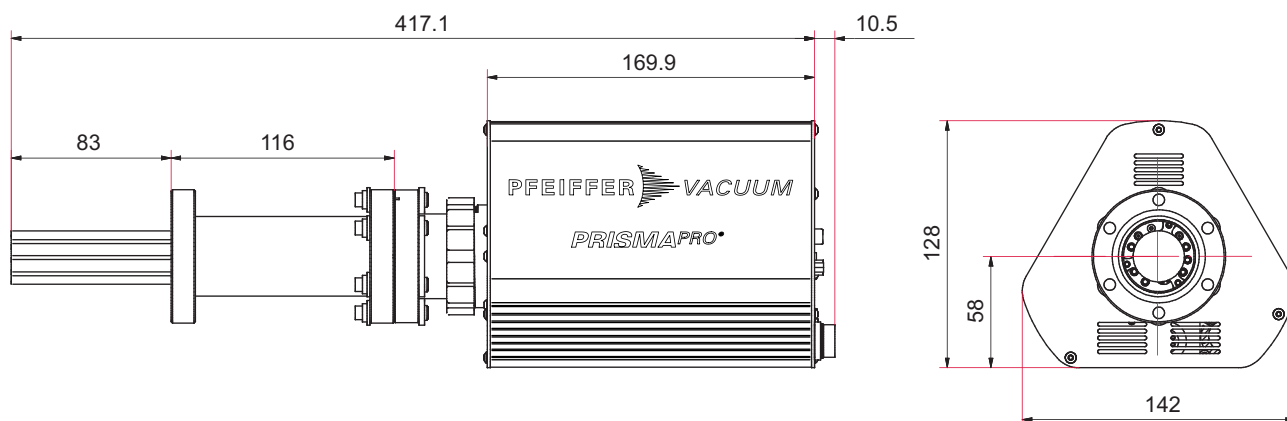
Dimensions QMG 250 M / SI ouverte / QME 250 rectiligne
